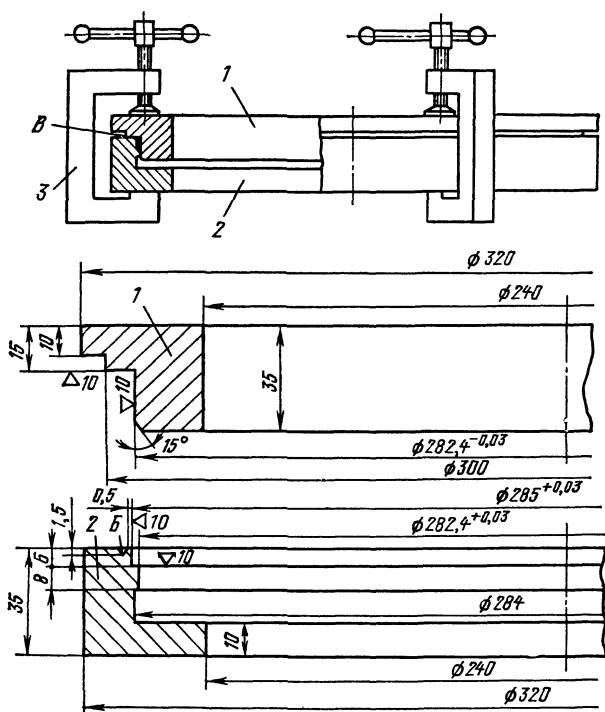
Конструкция пресс-формы для изготовления пассива.
